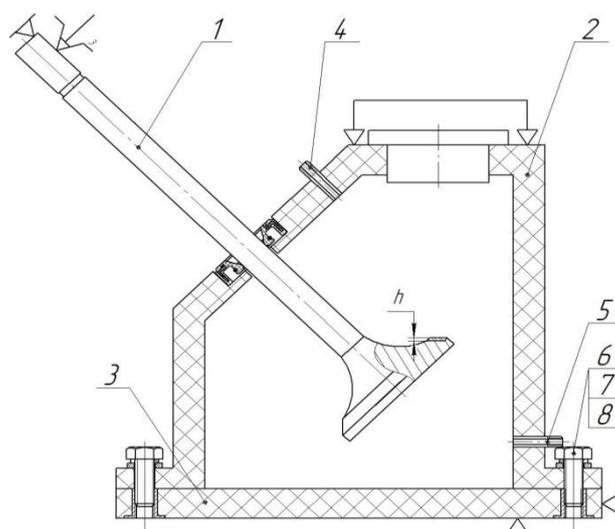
Схема установки для наплавки упрочняющего покрытия на рабочую фаску клапана
